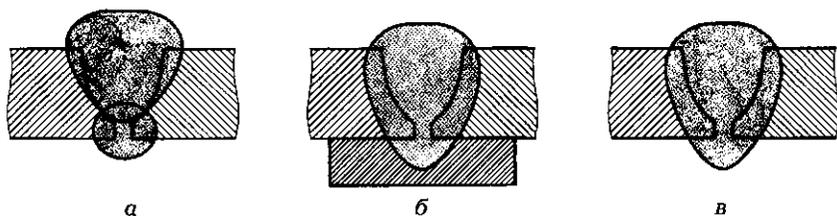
Стыковое сварное соединение с криволинейным скосом кромок: а — с двухсторонним сварным швом; б — с полным проваром на подкладке; в — с полным проваром
